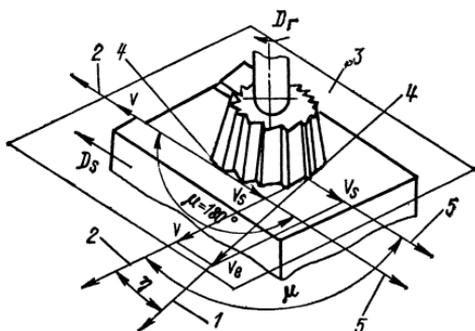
Элементы движений при фрезеровании концевой угловой фрезой:
